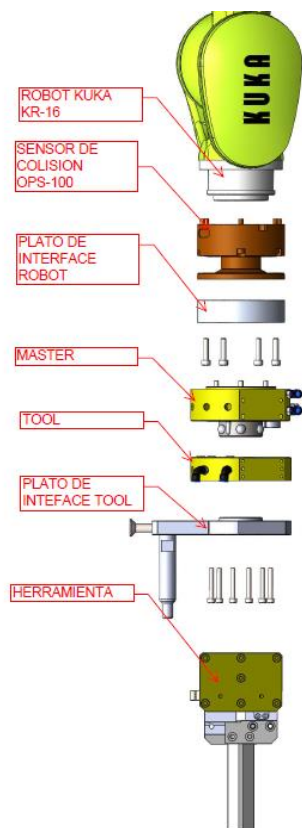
Montaje Plato interfaz del robot y Plato en "V"
